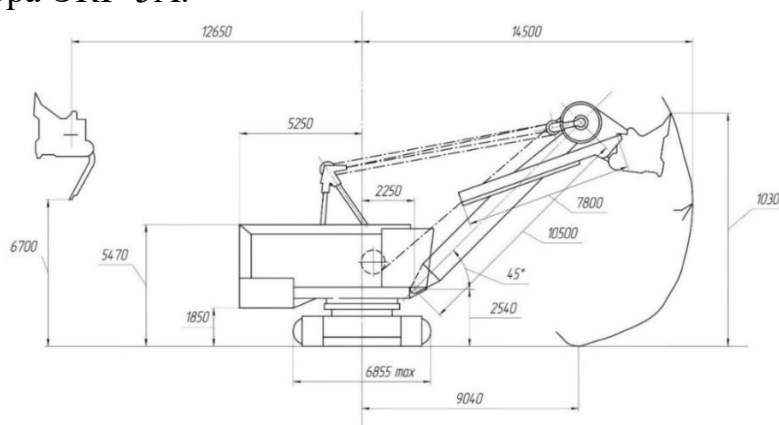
Габаритные и рабочие размеры экскаватора ЭКГ-5А
